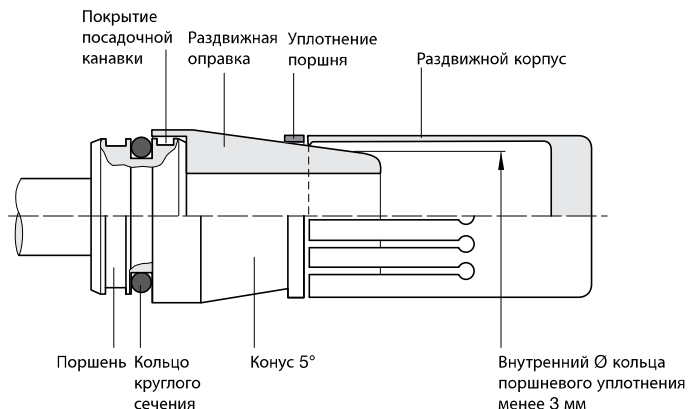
Slipper Seal®поршневого типа, установка, шаг 3. Комплект растягивающих инструментов для установки уплотнения Slipper Seal®поршневого типа.
